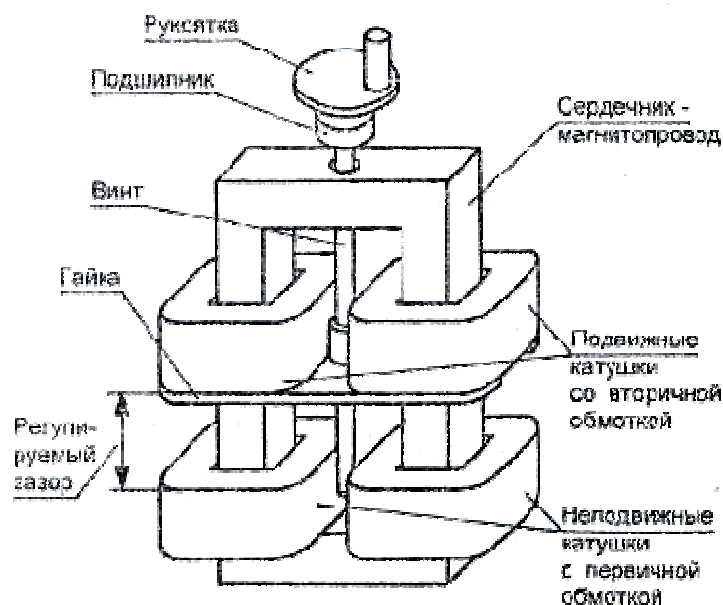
Конструктивная схема сварочного трансформатора с подвижными катушками вторичной обмотки
